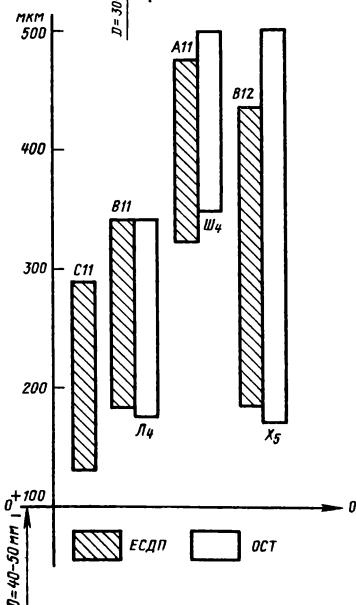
Поля допусков отверстий посадок с большими зазорами
